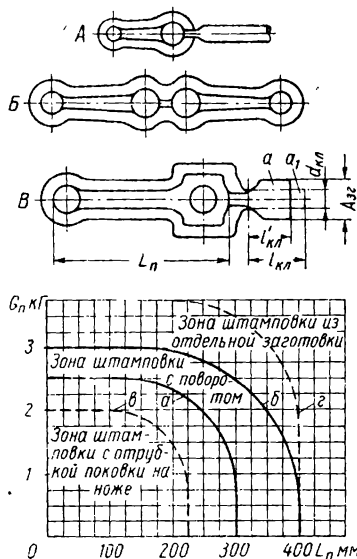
Диаграмма пределов применения различных заготовок: a — граница зоны применения заготовки на несколько поковок с отрубкой на ноже; b — граница зоны штамповки из заготовки на две поковки с поворотом, кривые v и $г$ дают расширенную зону штамповки с поворотом для поковок простых форм; L_n — наибольший габаритный размер поковки в мм; G_n — вес поковки в кг; $l_{кл}$ — длина клещевого конца в случае оттяжки клещевины; $l_{кл}$ — тоже без оттяжки клещевины; $A_{зс}$ — толщина исходной заготовки (по А. В. Ребельскому)
